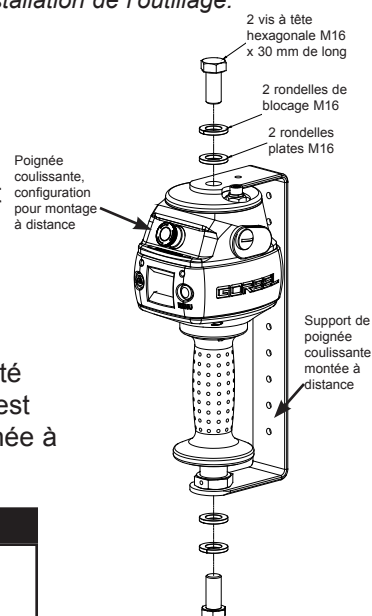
B3. Poignée coulissante montée à distance, vue éclatée.
